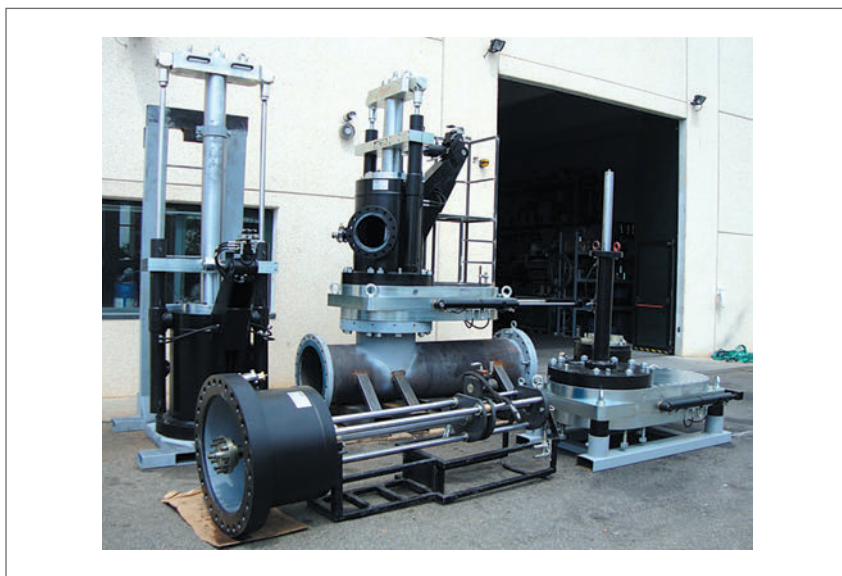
Оборудование для врезки и перекрытия нефте- и газопроводов Ду 600 мм
